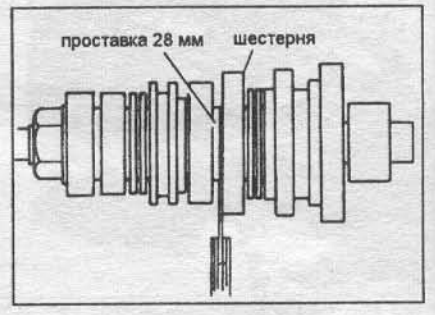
б Измерение осевого зазора шестерни 2-й передачи.
